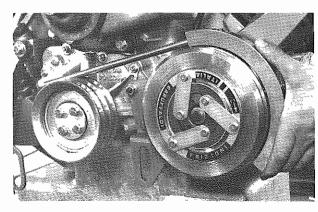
Allineamento pulegge albero motore-compressore Alignment of crankshaft-compressor pulleys
